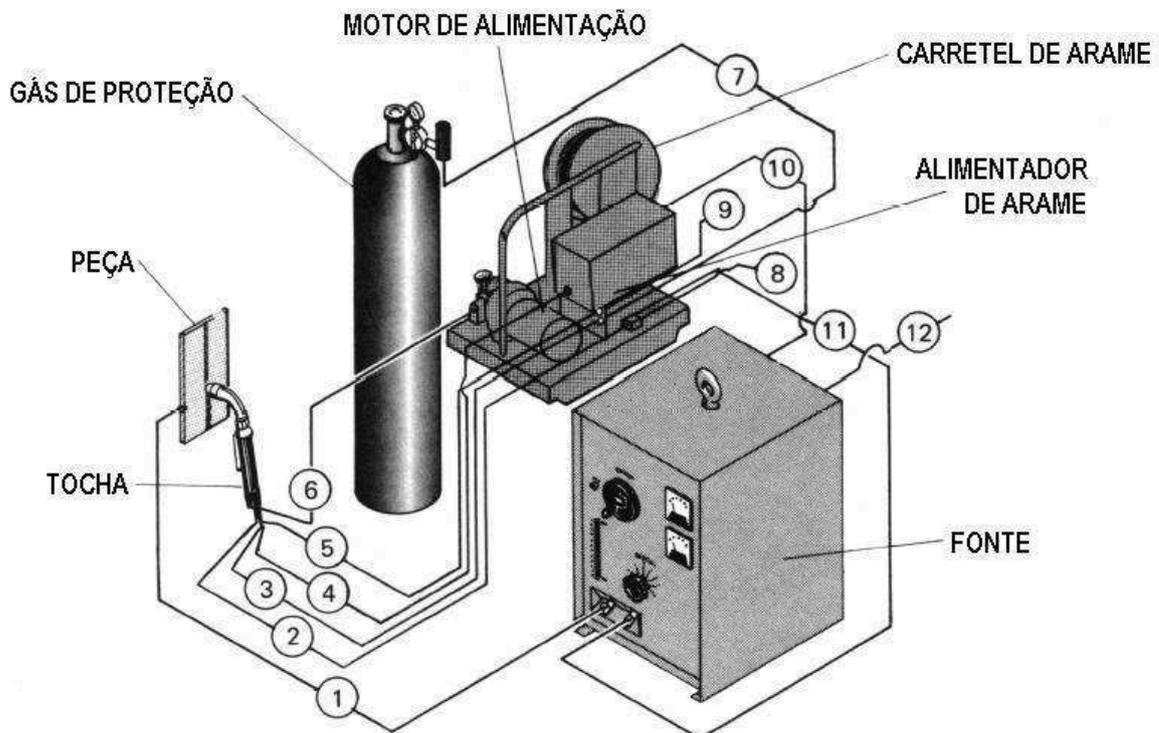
Instalações para a soldagem manual (ESAB MIG)
